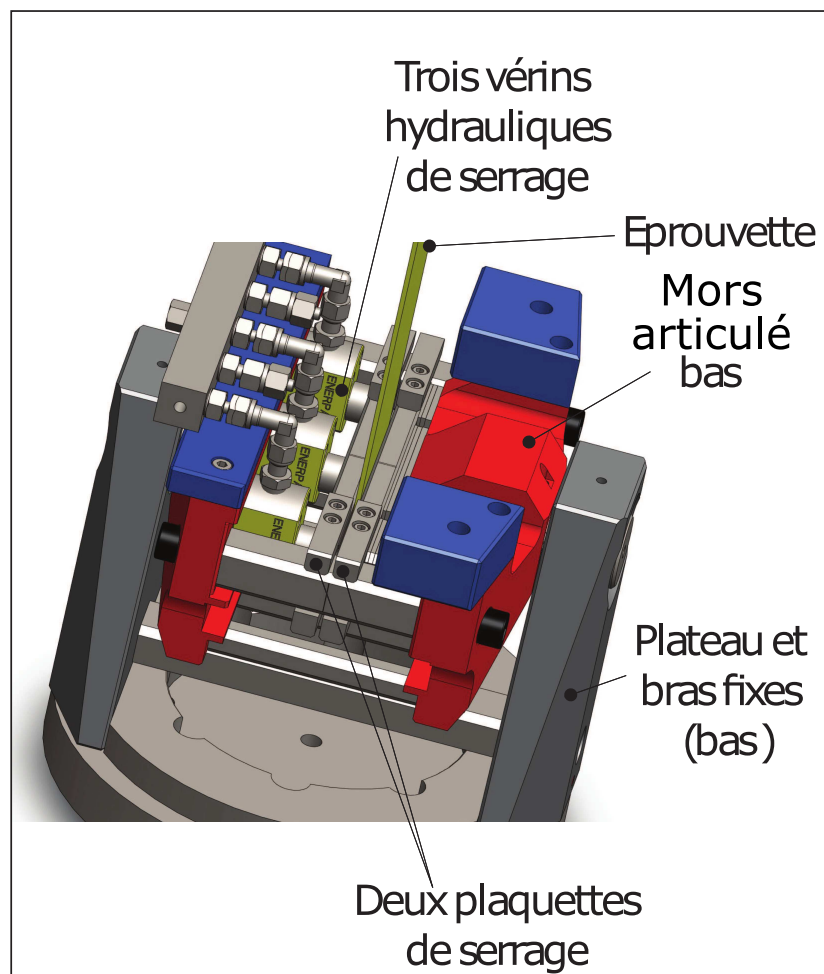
Serrage de l'éprouvette par trois vérins hydrauliques
